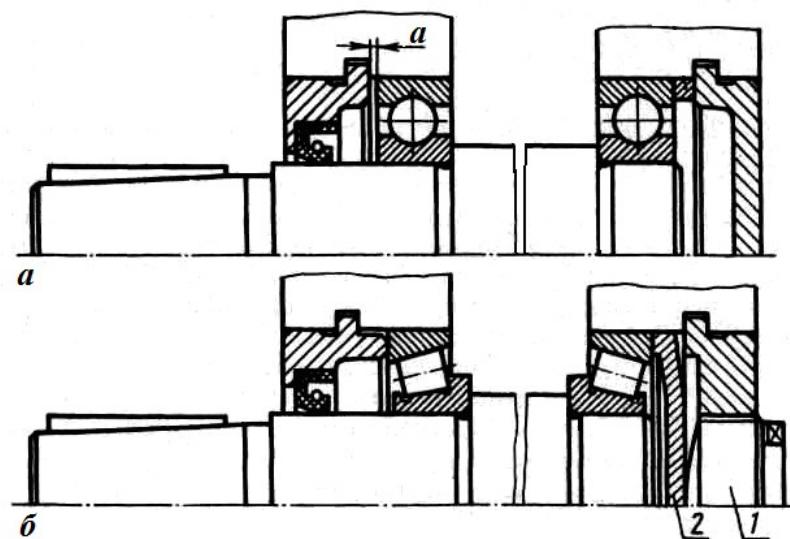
Установка подшипников, закрытых закладными крышками
